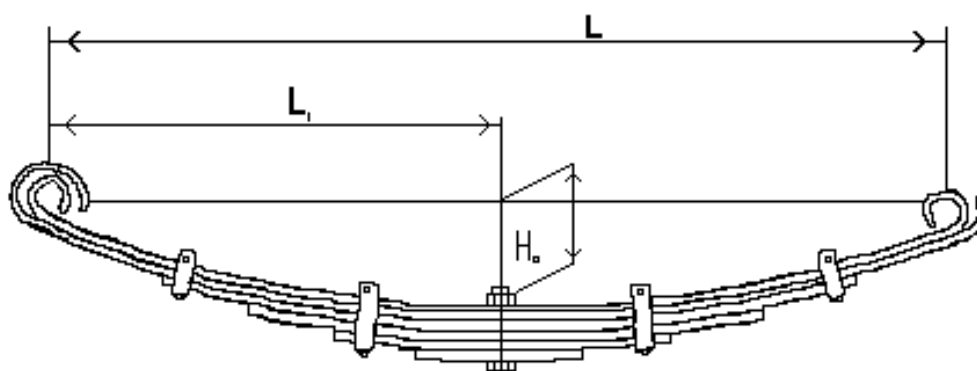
Чертеж полуэллиптической рессоры
